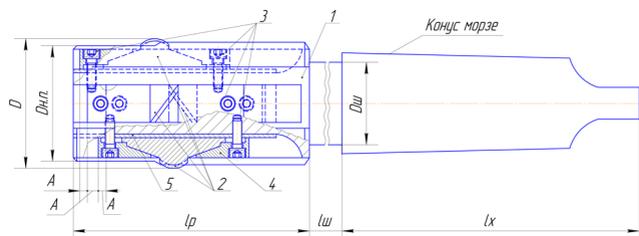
Общий вид резцовой сборной развёртки с безвершинными зубьями
